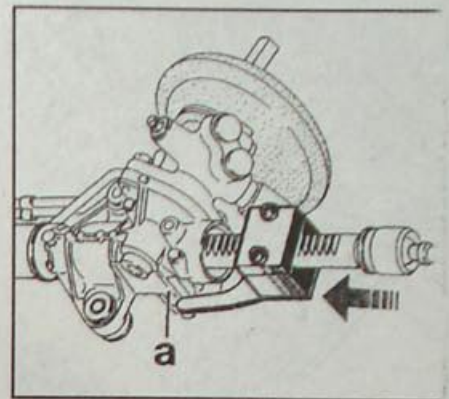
Введение приспособления Dir. 1306-02 картер (а) рулевой передачи
